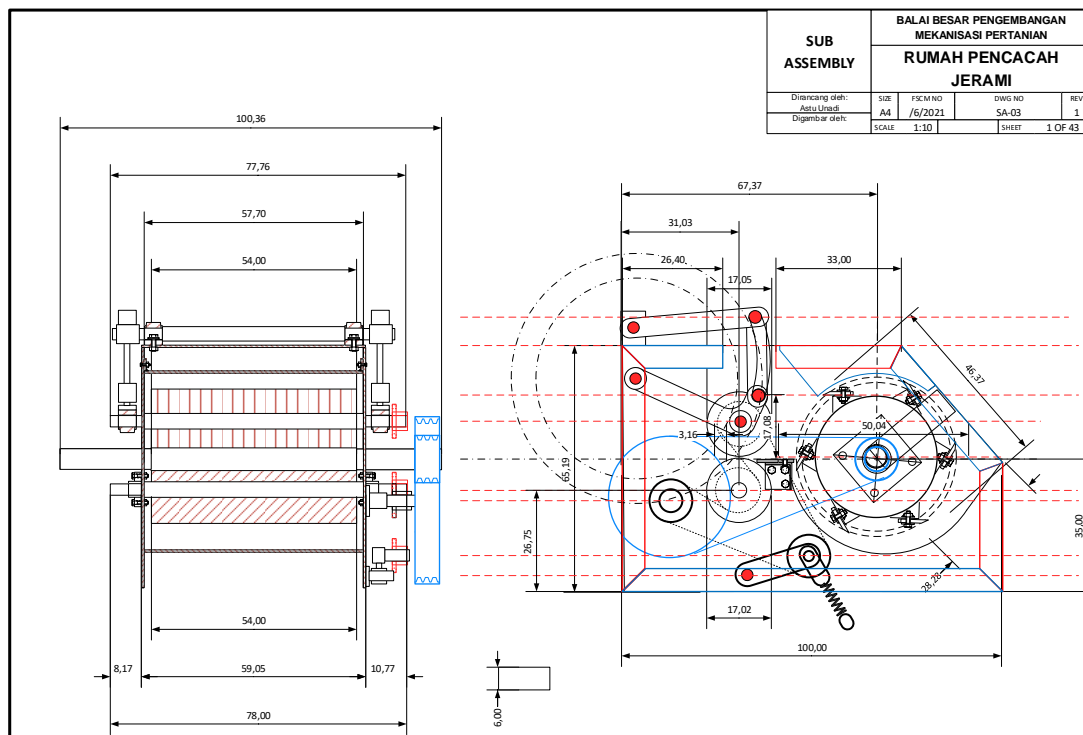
Rakitan bagian mesin pencacah dan motor penggerak
